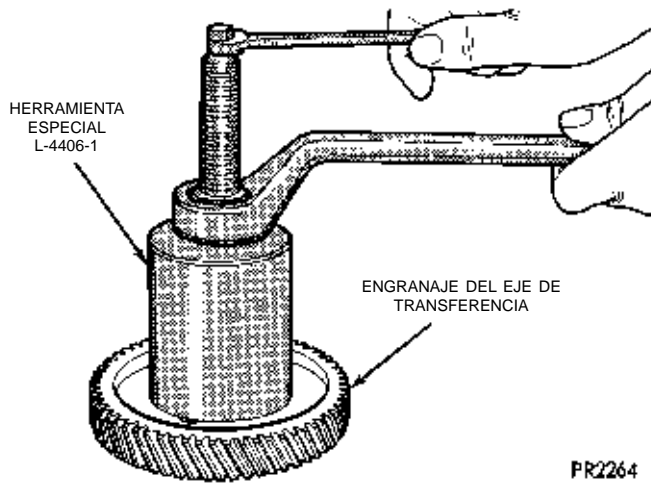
Mediante la Herramienta L-4406-1 con el Adaptador L-4406-3, retire el cono del cojinete del engranaje del eje de transferencia
